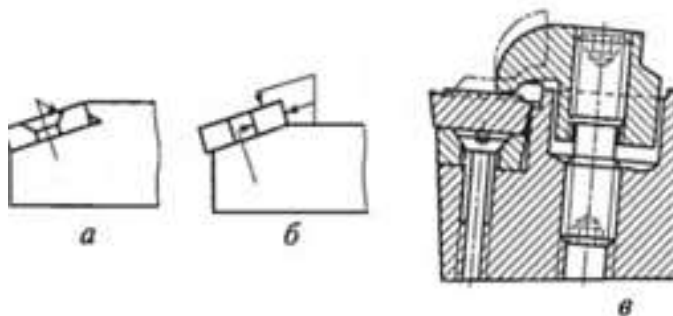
Резцы, оснащенные многогранными пластинами из твердого сплава
